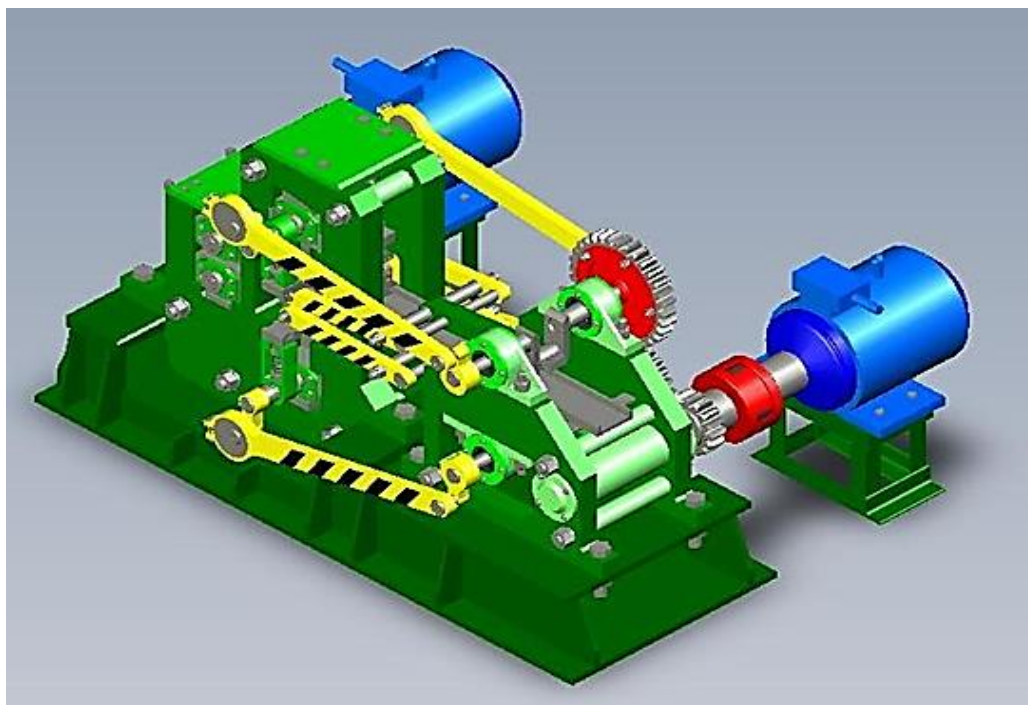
Общий вид маятникового стана с опорной профилированной планкой
